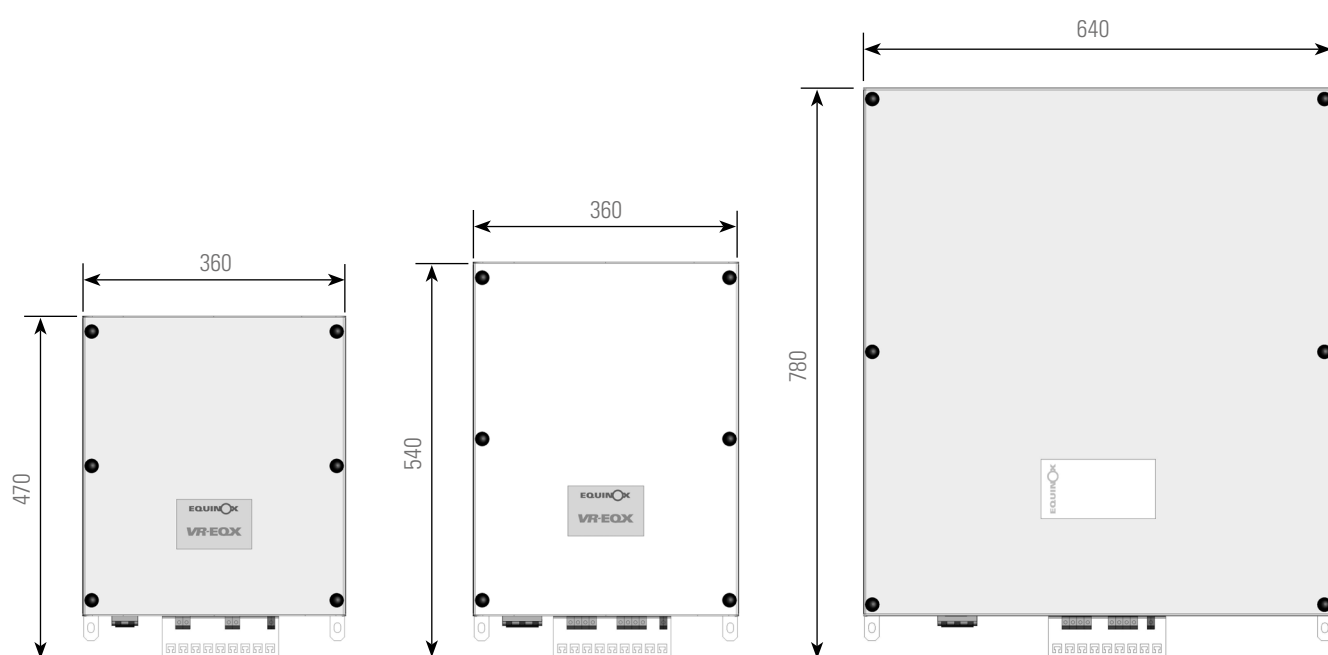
Aspecto y dimensiones, de izqda. a dcha. de los modelos de 3-6 kW, 10-20 kW y 30 kW.
